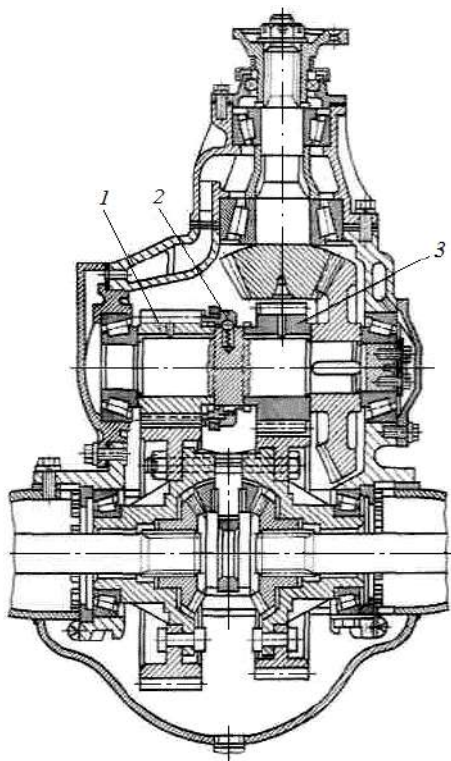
Двоступінчасті ГП з циліндричною зубчастою передачею:
